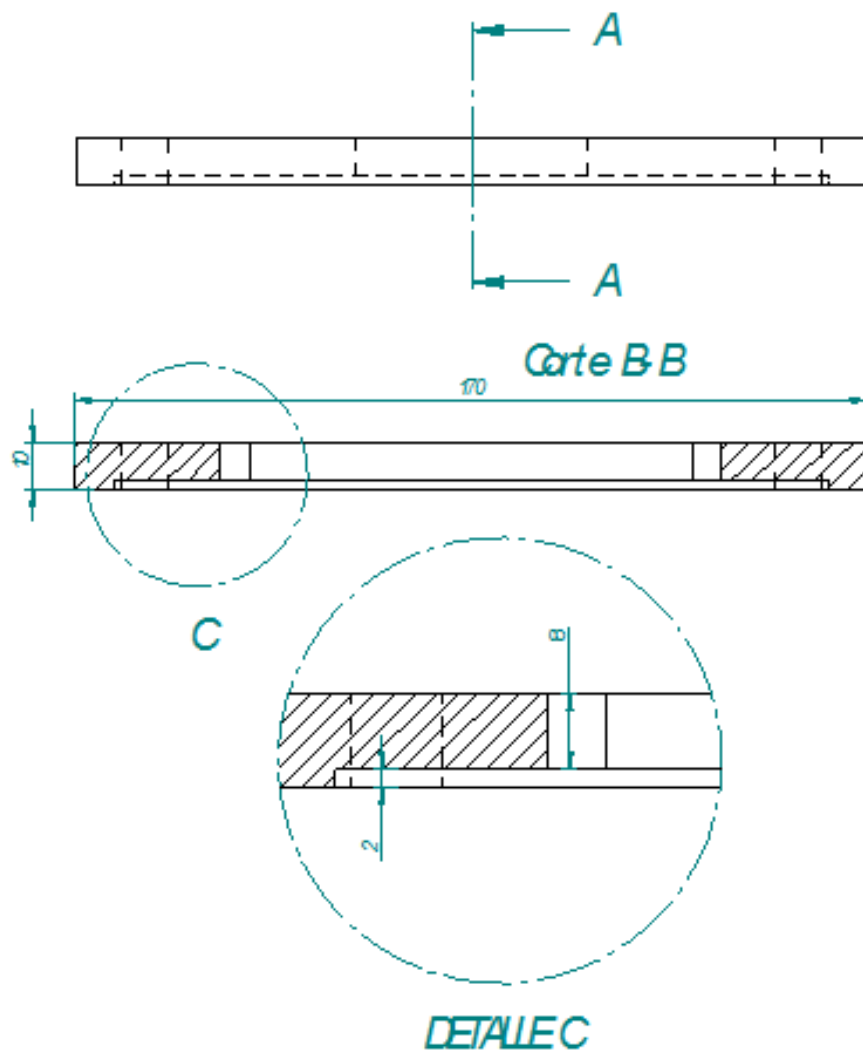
Plano de Tapa superior. A) Vista exterior. B) Vista Inferior
